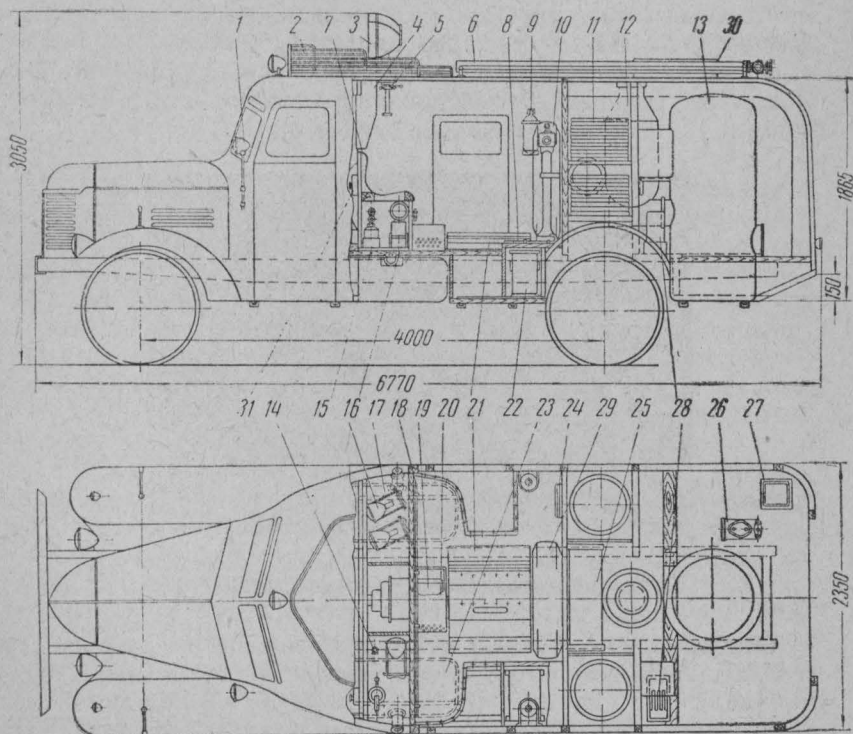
Размещение оборудования на паровой установке ПУ-1:
